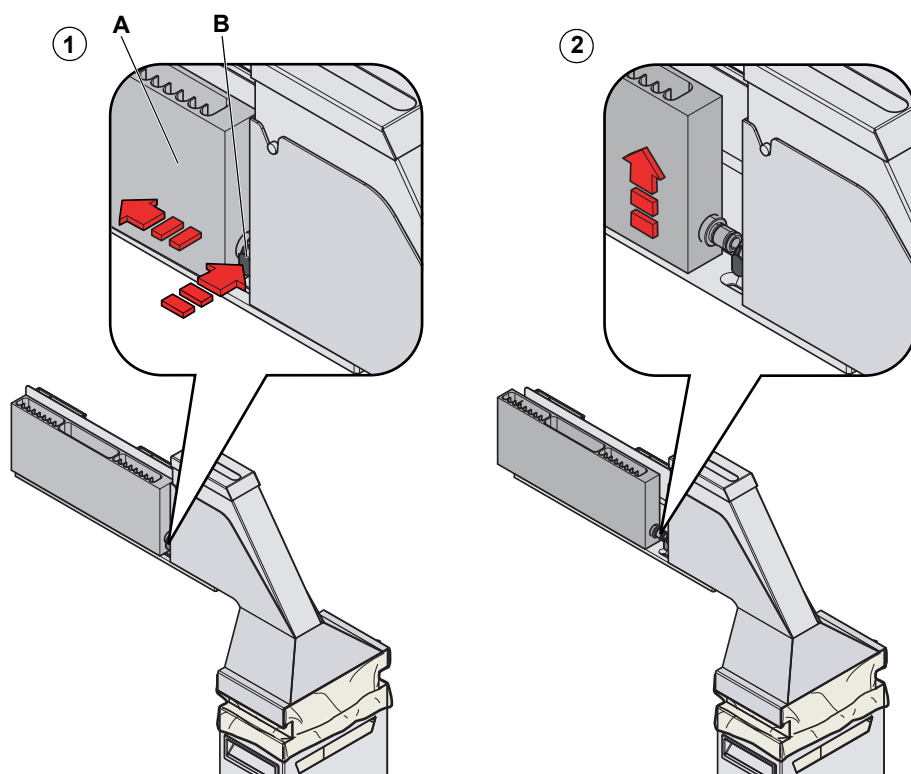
Rimozione della stazione di lavaggio dal piano di lavoro
